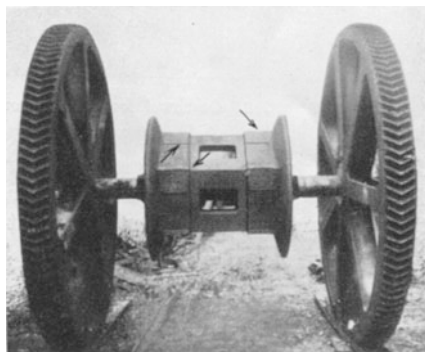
Auftragsschweißung an einer Kettentrommel.
